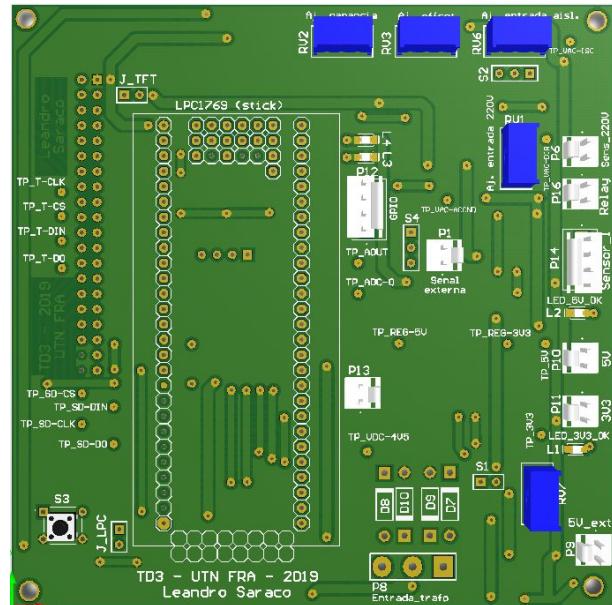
Vista en 3D de la Placa principal realizada mediante Altium Designer v16.
